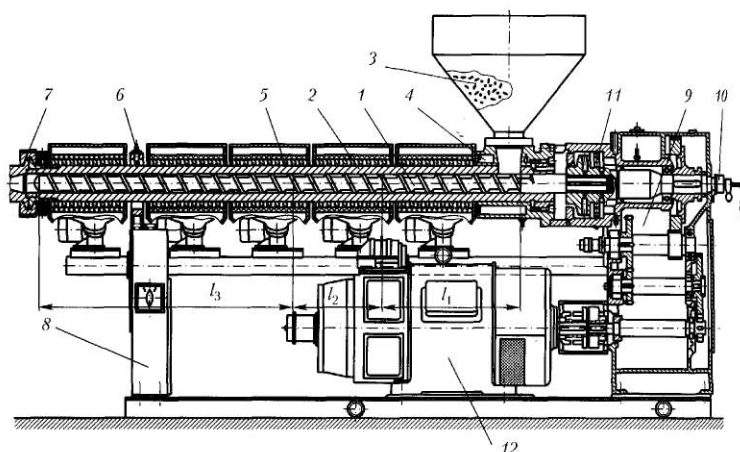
Принципиальное устройство одношнекового экструдера: 1 – шнек, 2 – материальный цилиндр, 3 – бункер, 4 – каналы, 5 – зонные кольцевые нагреватели, 6 – термопары, 7 – формующая головка, 8 – массивный корпус, 9 – механическая передача, 10 – патрубок для отвода охлаждающей воды, 11 – подшипниковый узел, 12 – электродвигатель
